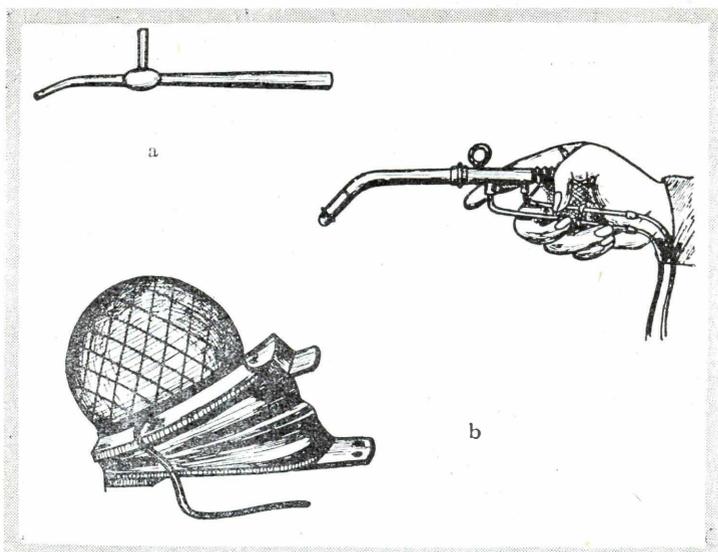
Tipo di pipetta che può servire per aria e gas. Il tubo del gas è fissato alla presa laterale, mentre il tubo dell'aria è portato alla apertura posteriore. In b un altro tipo. In basso un soffietto a pedale.
